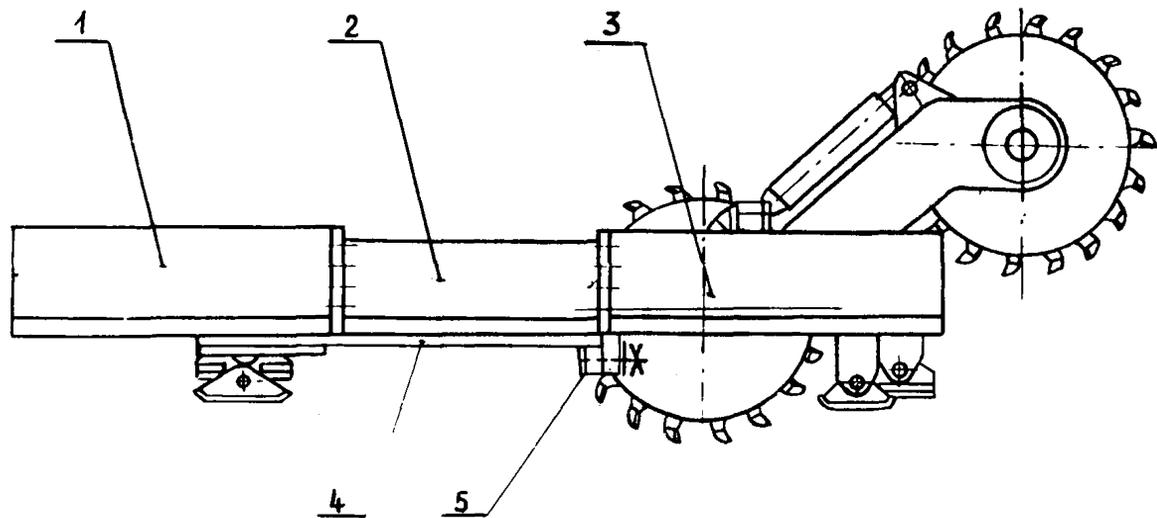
Усиление соединения электродвигателя с подающей и режущей частями комбайна КШ-1КГ с помощью дополнительной стальной плиты:
